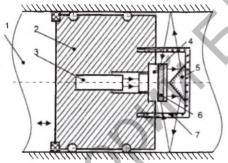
Принципиальная схема оптико-механического устройства для контроля: 1 - контролируемая поверхность, 2 - перемещаемый модуль, 3 - лазер, 4 - телескоп, 5 - коническое зеркало, 6 - кольцевая ПЗС-матрица, 7 - стеклянный стакан
